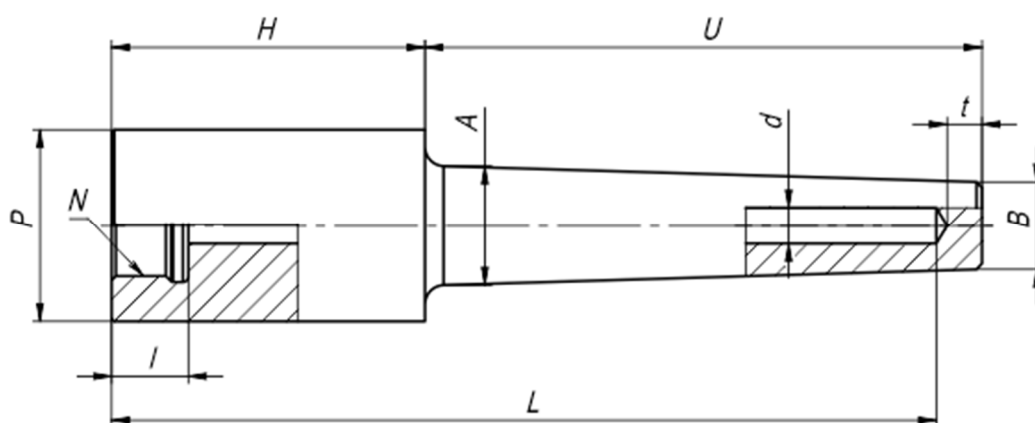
Гильза под приварку через адаптер (Socket Weld), цельноточёная, коническая, под неподвижный штанцер.
